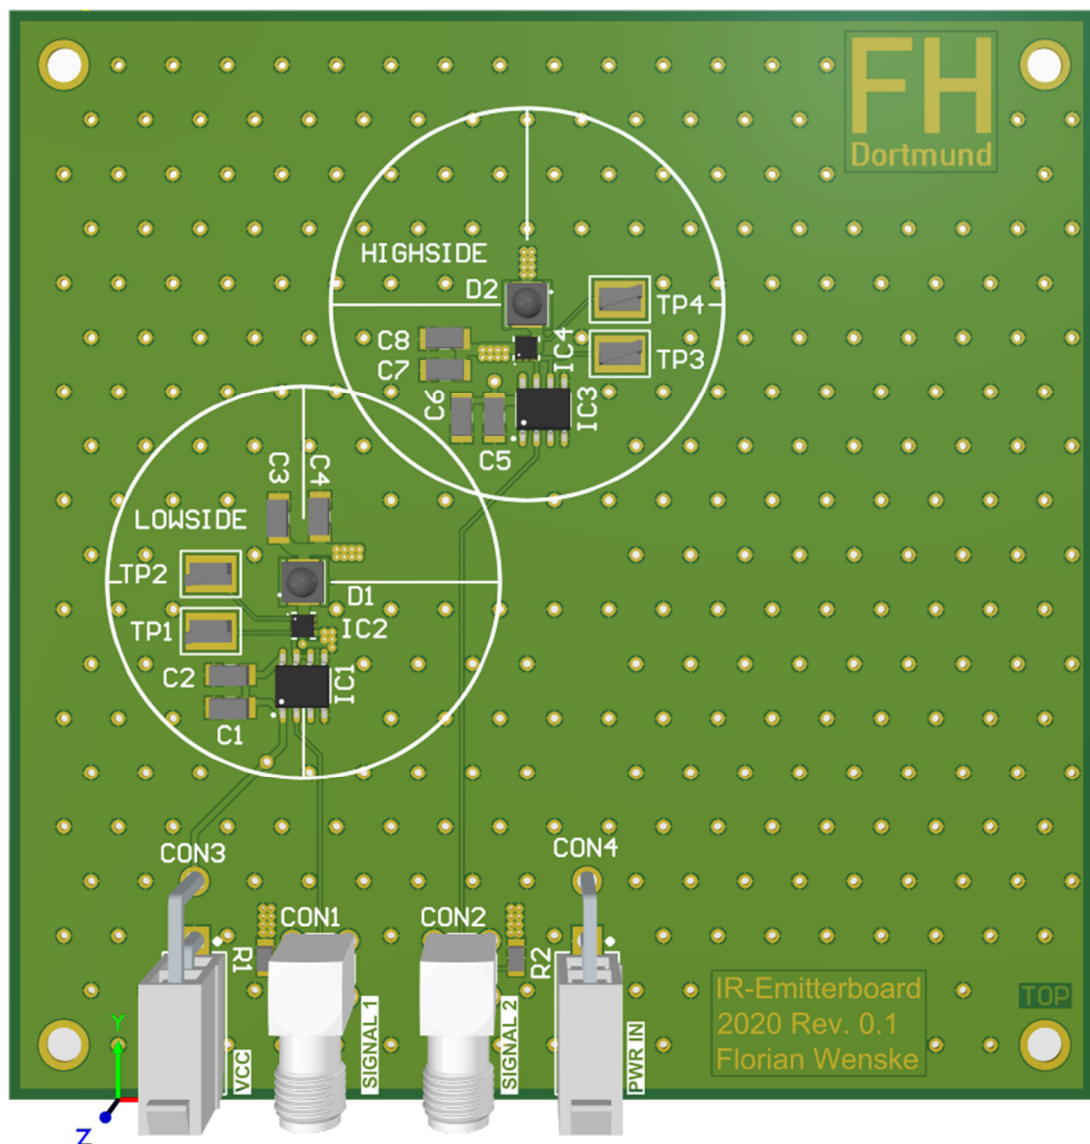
Finales PCB-Layout in 3D-Ansicht
